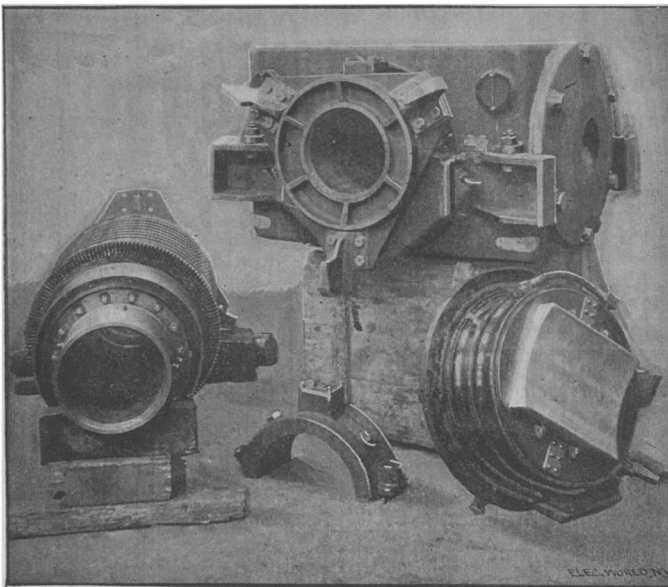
Locomotive Heilmann. — Pièces détachées d'un moteur.
